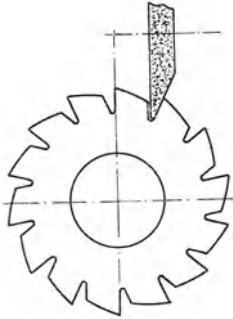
Das Schleifen hinterdrehter Fräser an der Zahnbrust.
